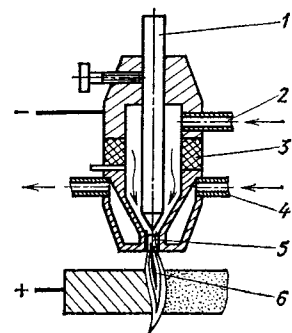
Схема плазменно-дуговой резки; 1 — катод; 2 — подача газа; 3 — изолятор; 4 — система охлаждения; 5 — сопло; 6 — дуга и струя плазмы
